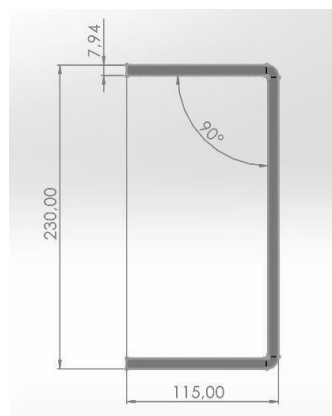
Perfil plegado elegido para la estructura de la mesa soporte
